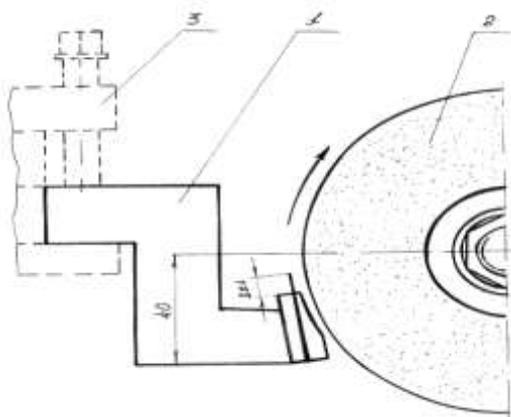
Опытная установка для подготовки к работе тонких пластинчатых ножей .1 – ножедержатель; 2 – заточной вал; 3 – резцедержатель станка.
